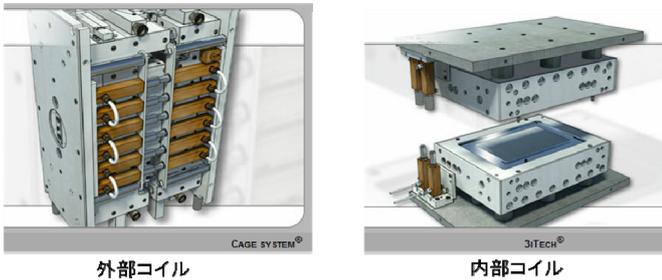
ロックツール社の誘導加熱による金型加熱冷却システム
